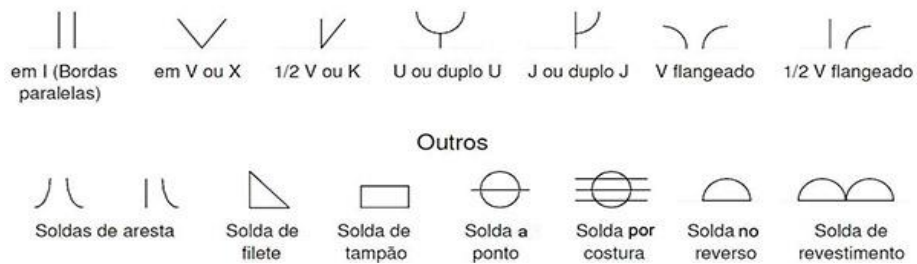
Símbolos básicos de soldas. (Fonte: Soldagem: fundamentos e tecnologia / Paulo Villani Marques, Paulo José Modenesi, Alexandre Queiroz Bracarense – 3ª edição atualizada – Belo Horizonte: Editora UFMG, 2009)
